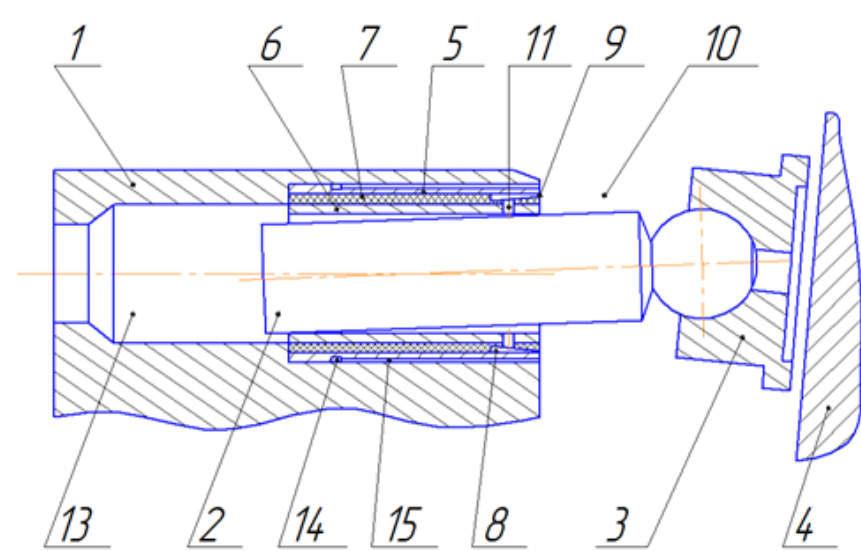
Циліндр аксіально-поршневої гідромашини: 1- блок циліндрів; 2-плунжер; 3-пята; 4-похилий диск; 5- зовнішня втулка; 6-внутрішня втулка; 7-пружно-демпфуючий елемент; 8- розвантажувальні камери; 9- отвір з'єднаний з дренажною магістраллю; 10-внутрішня порожнина гідромашини; 11-отвір, з'єднаний з внутрішньою поверхнею втулки; 12- отвори, розміщені у втулці зі сторони робочої камери; 13- робоча камера; 14- кільцевий канал зовнішньої втулки; 15- повздовжній канал.
